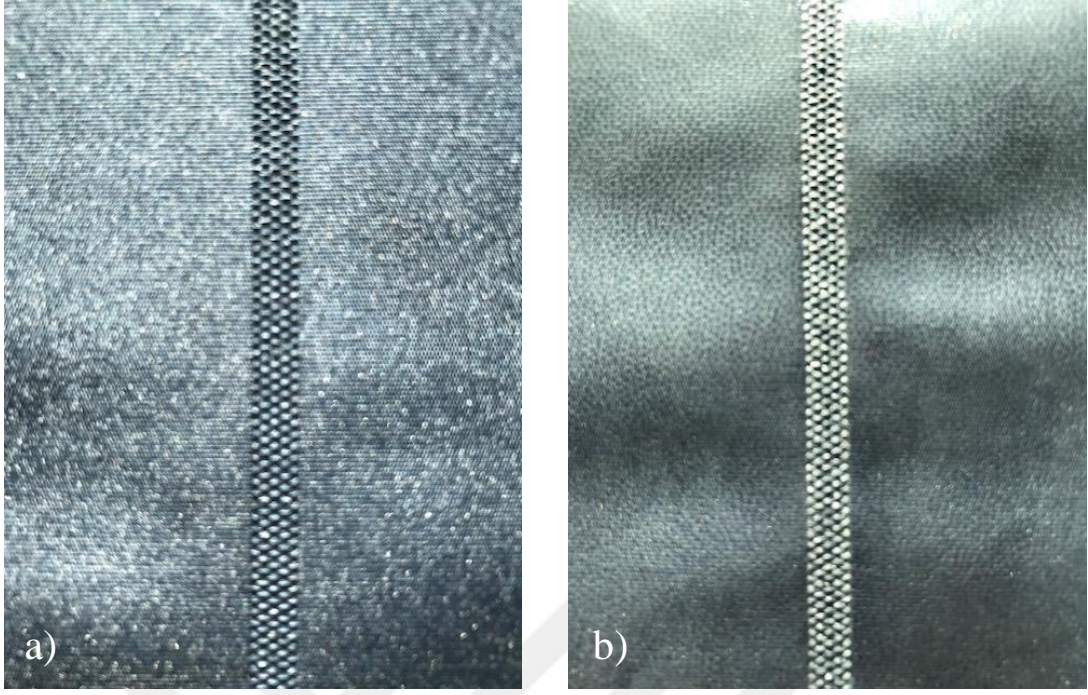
Ultrasonik dikiş makinesinde R1 ile dikilen D1 kumaşının görüntüsü
